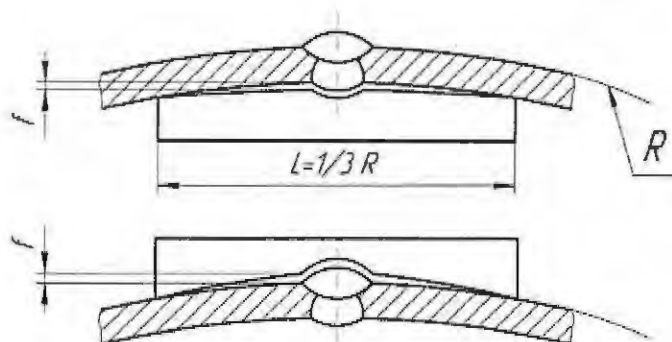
Схема замера угловатости сварного шва и отклонения формы детали от теоретической окружности в околошовной зоне.
